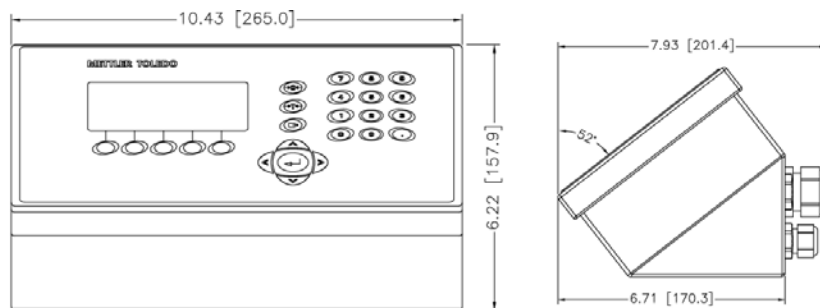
Dimensioni del montaggio a pannello dell'IND560 PDX
